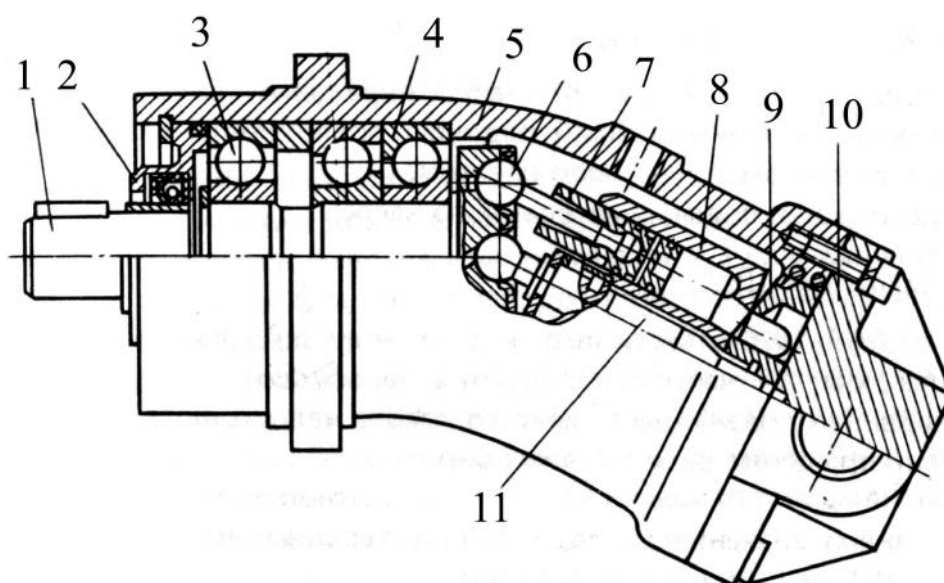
Аксиально-поршневой насос (нерегулируемой подачи) с наклонным блоком: 1 – приводной вал; 2 – передняя крышка; 3, 4 – радиальные шариковые подшипники; 5 – корпус; 6 – шатун; 7 – поршень; 8 – блок цилиндров; 9 – сферический распределитель; 10 – крышка; 11 – центральный шип
